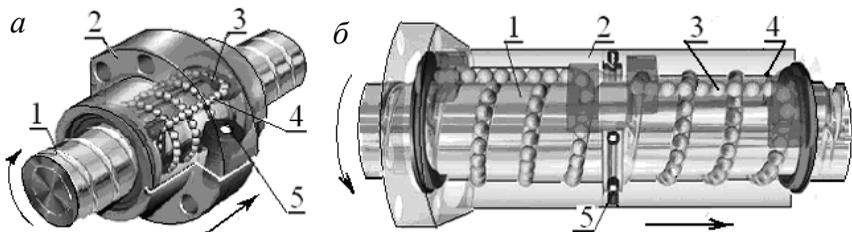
Схемы работы передачи винт-гайка качения с циркуляцией шариков с одной (а) и двумя гайками (б)
